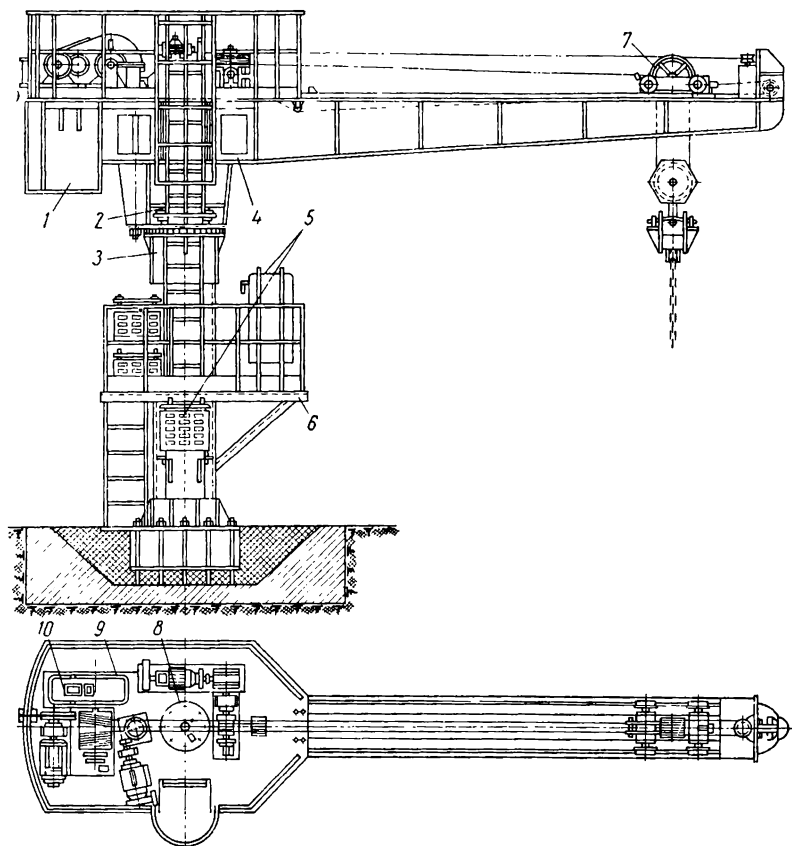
Общий вид ковочного поворотного крана: 1 — противовес; 2 — ролики; 3 — опорная колонна; 4 — сварная консольная стрела; 5 — аппаратура управления краном; 6 — площадка управления; 7 — тележка; 8 — подпятник оси колонны; 9 — механизм поворота крана; 10 — механизм подъема груза
